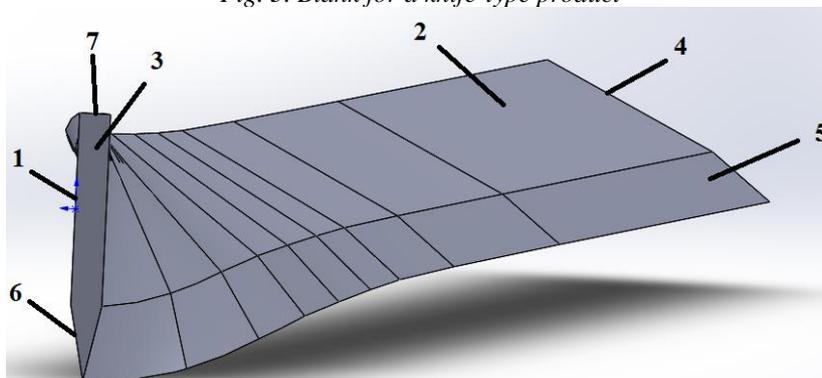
Обозначение обрабатываемых поверхностей детали «нож»
